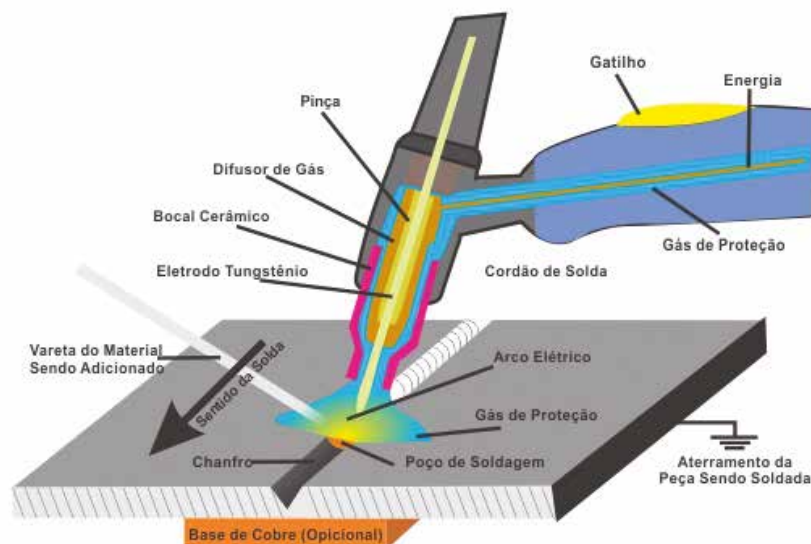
Processo de solda TIG. Fonte: Portal Metalica.
